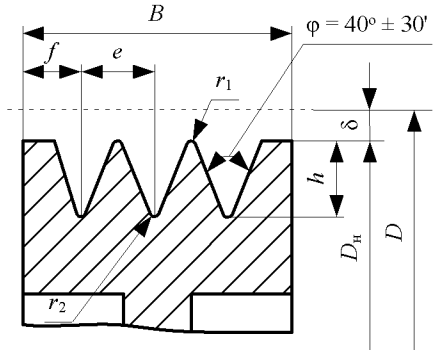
Размеры канавок шкива поликлиноременной передачи
